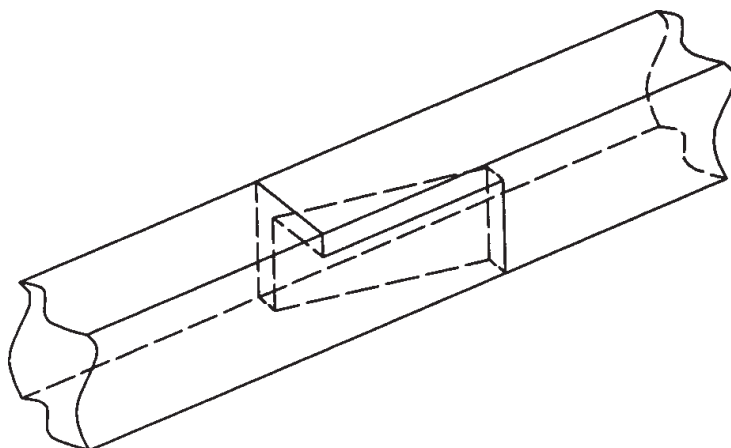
Unión de piezas de la quilla con escarpe vertical parcial, utilizado en el norte de Portugal.
